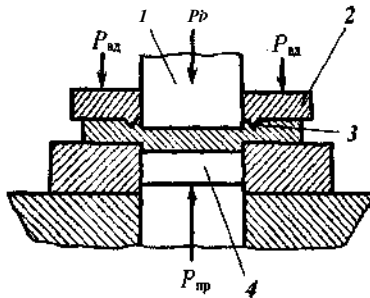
Схема чистовой вырубке с поперечной осадкой заготовки: 1 - пуансон; 2 - прижим; 3 - клиновое ребро; 4 - выгалькатель
